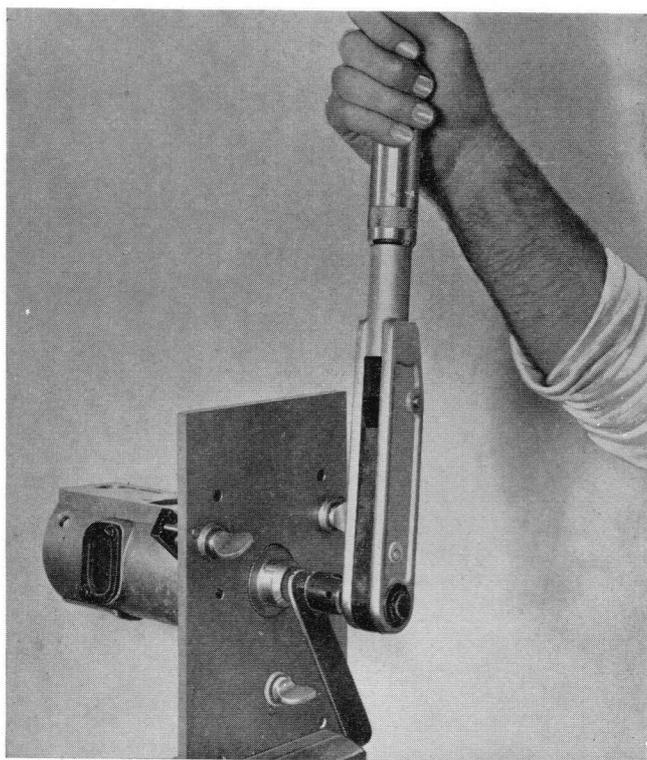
Serrage ou desserrage de la vis de fixation du moyeu d'entraînement
